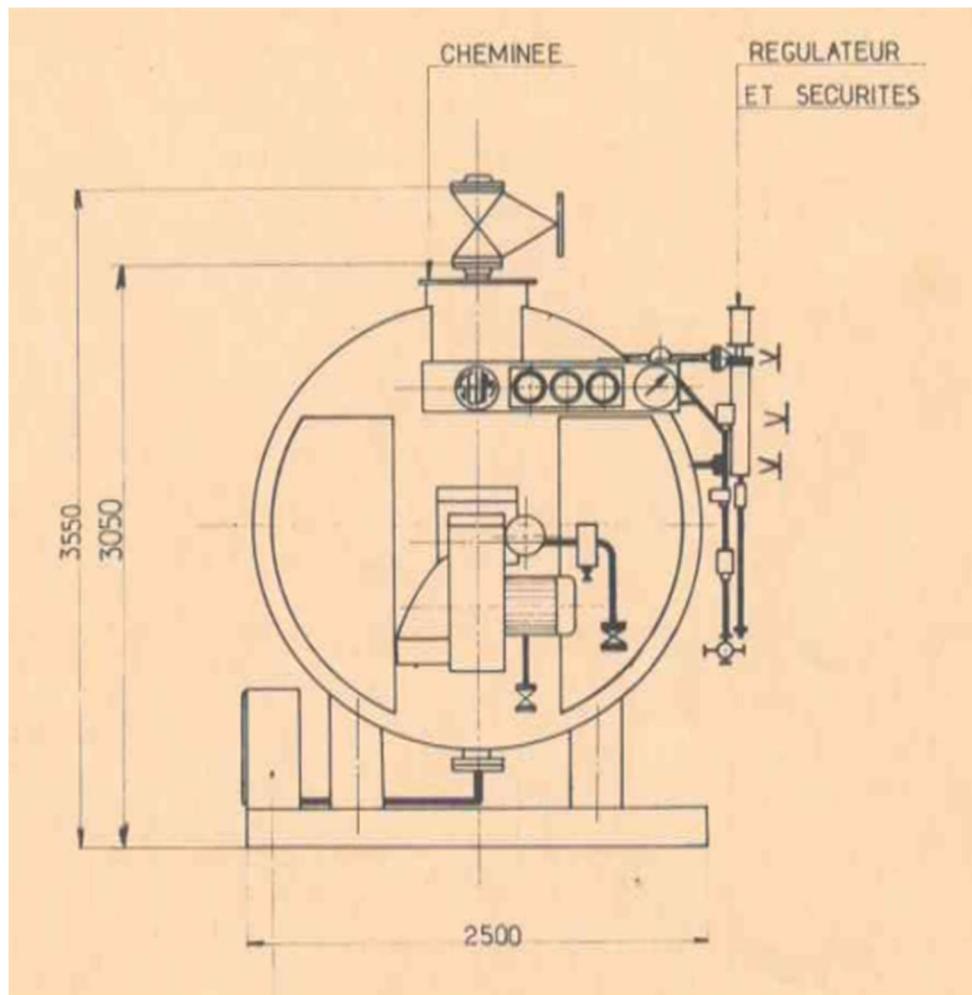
Vue de face de la chaudière SEUM NX 75 [2]
